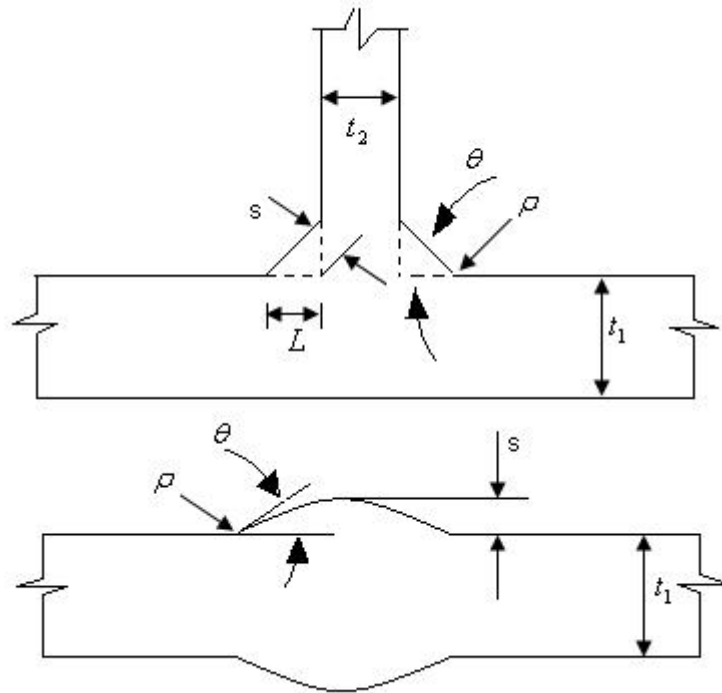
Parámetros que definen la geometría nominal de la soldadura. Ref. [22]
